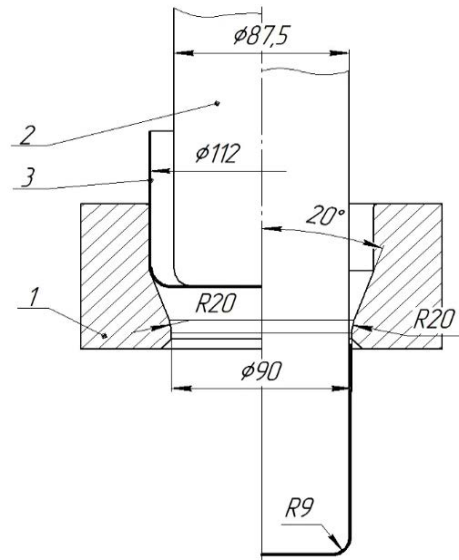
Схема другої витяжки: 1 – матриця, 2 – пуансон, 3 – заготовка
